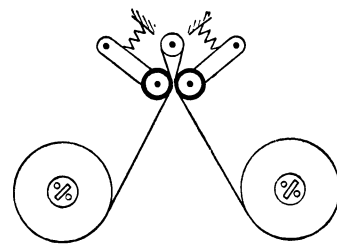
Приспособление для полировки рабочей поверхности ленты.
